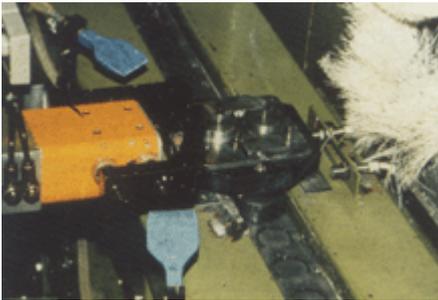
Abblasvorrichtung an einer Universal-Werkzeugmaschine zum Entfernen von Spänen und Kühlflüssigkeit. Pegelminderung von 98 auf 85 dB(A)
